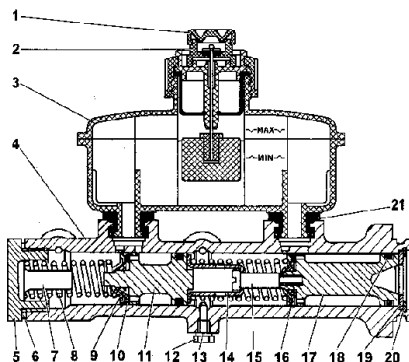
Главный тормозной цилиндр: 1 -защитный колпачок; 2 -крышка с датчиком аварийного уровня тормозной жидкости; 3 -бачок; 4 -картер главного тормозного цилиндра; 5 -пробка; 6,13-прокладки; 7 -вкладыш пробки; 8 -пружина; 9 -седло пружины; 10,19-шайбы; 11,17-поршни; 12 -болт упорный; 14 -втулка-ограничитель; 15 -винт-упор; 16 - манжета уплотнительная; 18 -наружная манжета; 20 -стопорное кольцо; 21 -втулка соединительная
